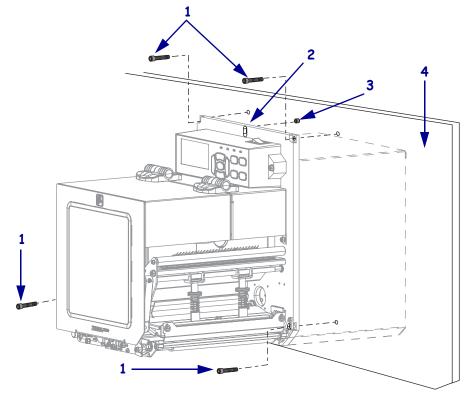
• Vista frontale del motore di stampa nell'applicatore
